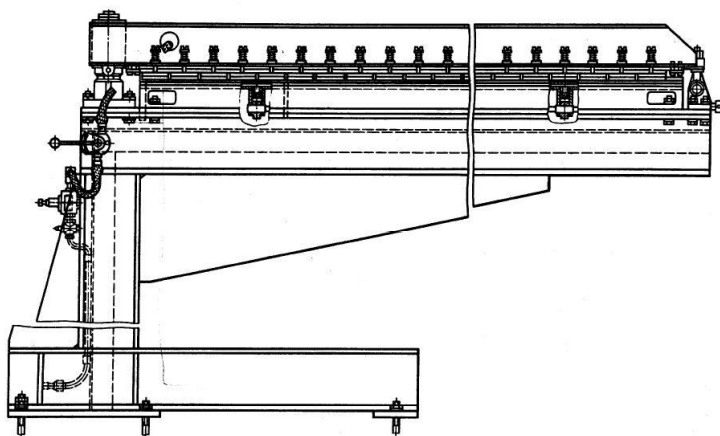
Стенд для зварювання поздовжніх швів
